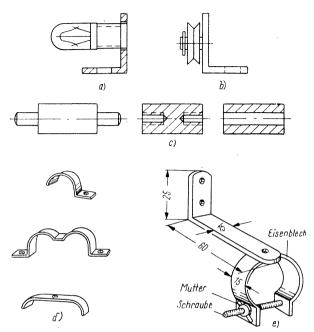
Befestigungsteile a) Winkel für Skalenlampe, b) Winkel für Seilrolle, c) Abstandsstücke, d) Befestigungsschellen für Elkos usw., e) Halterung für ein magisches Auge (z. B. 6 E 5)
